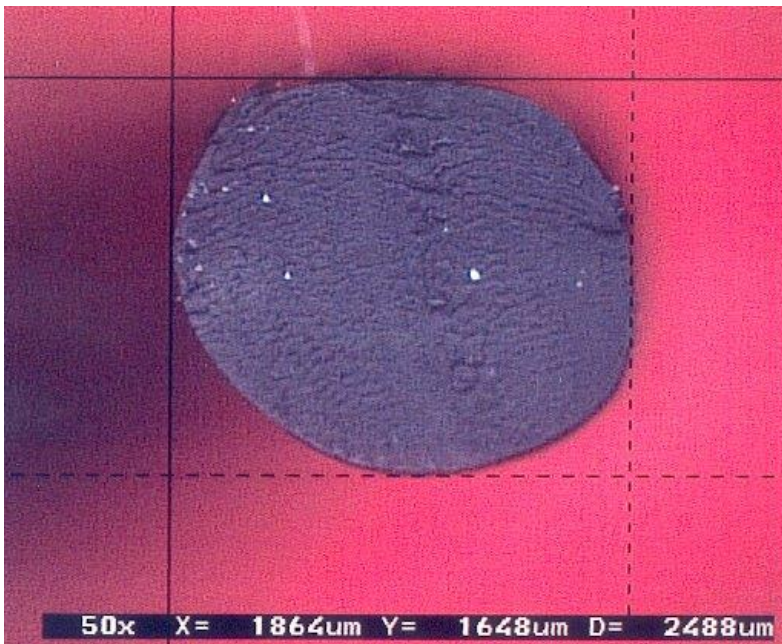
Einseitig durch Abrieb abgeflachter O-Ring („statische“ Abdichtung)
